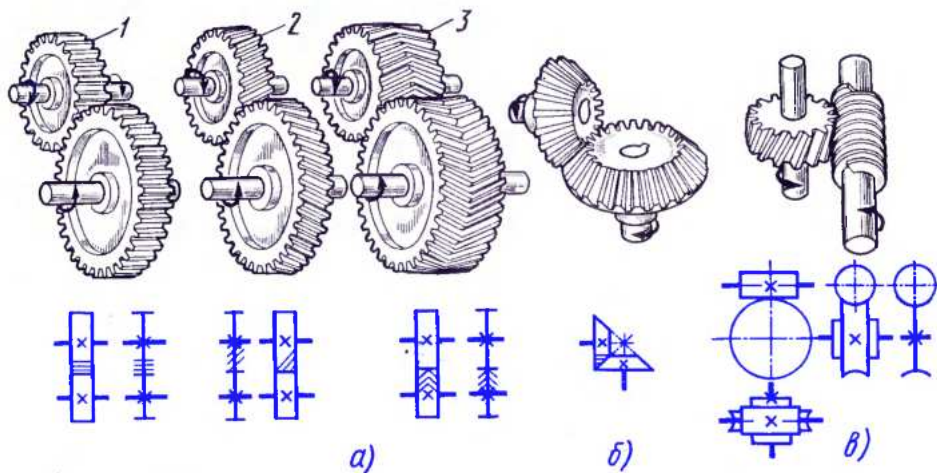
Передачи автомобильных кранов и их обозначение на схемах: а — зубчатые цилиндрические с прямыми (1), косыми (2) и шевронными (3) зубьями, б — зубчатая коническая с прямыми зубьями, в — червячная
